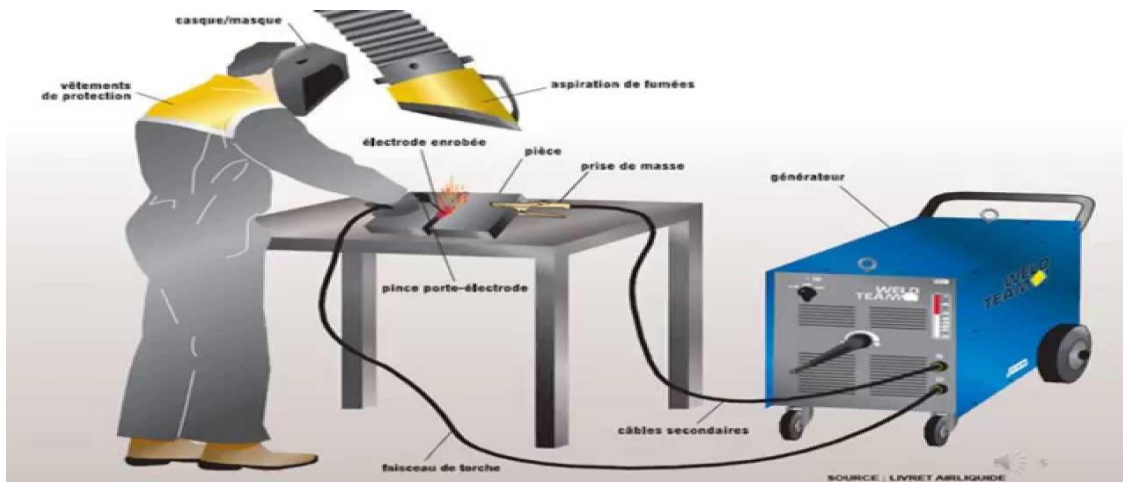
le principe de Soudage à l'arc avec électrode enrobée.
